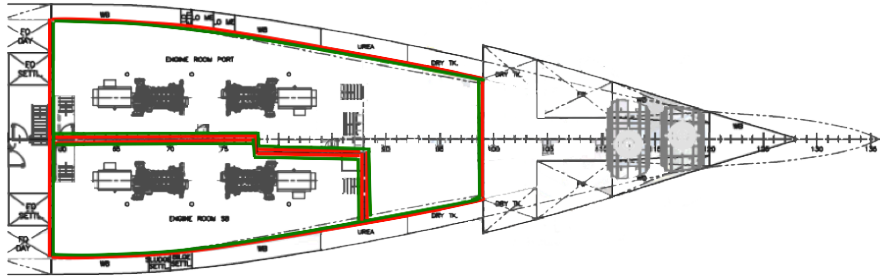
Aislamiento de la sala de máquinas: mamparos.
